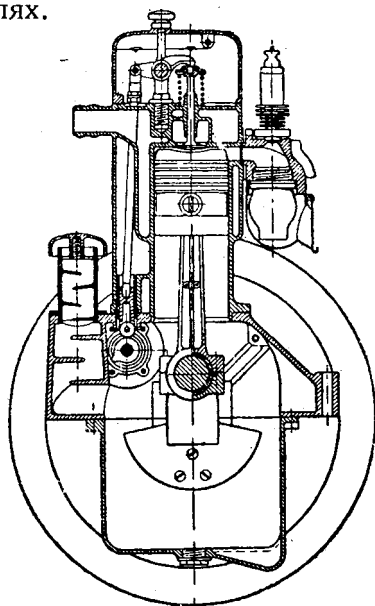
Продольный разрез двигателя Баньюло (старой конструкции).
